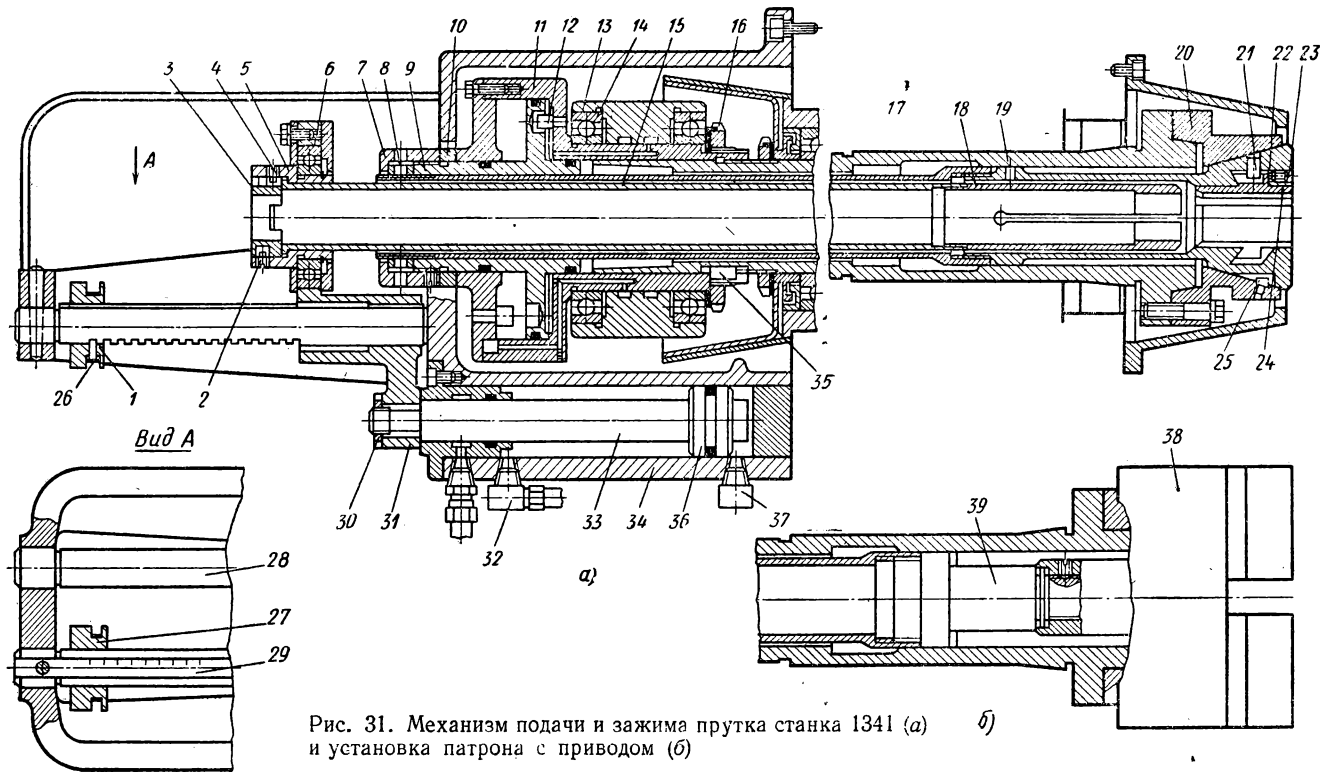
Механизм подачи и зажима прутка станка 1341 (а) и установка патрона с приводом (б)
